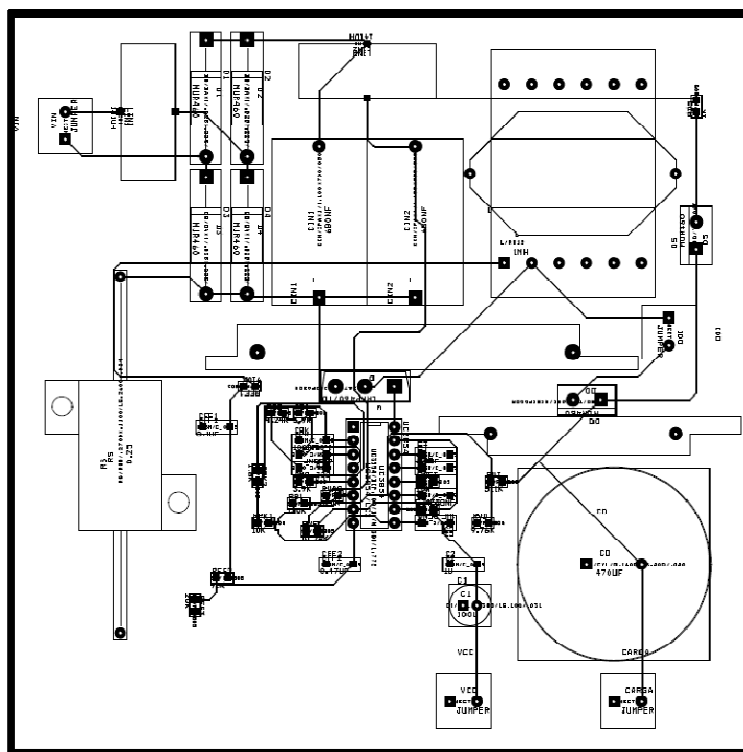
16 Placa PCB componentes colocados, borde de placa y rutado de pistas.
